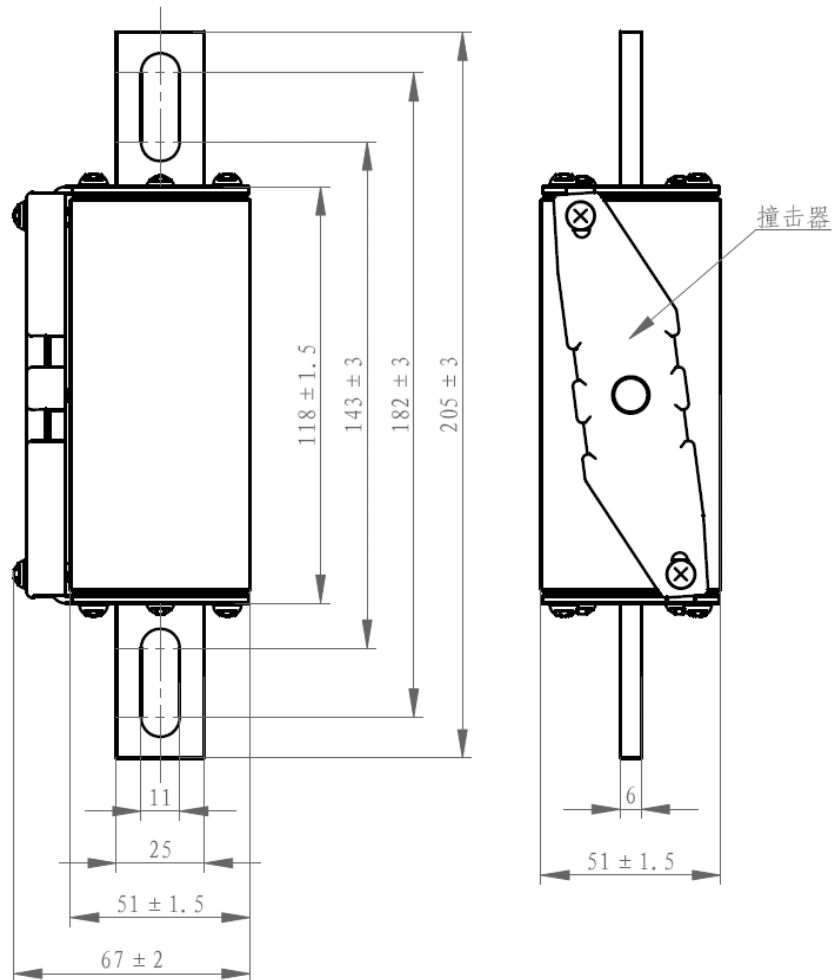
STFG10-1000/400/C2 腰形孔型螺栓连接的外形尺寸和安装尺寸
